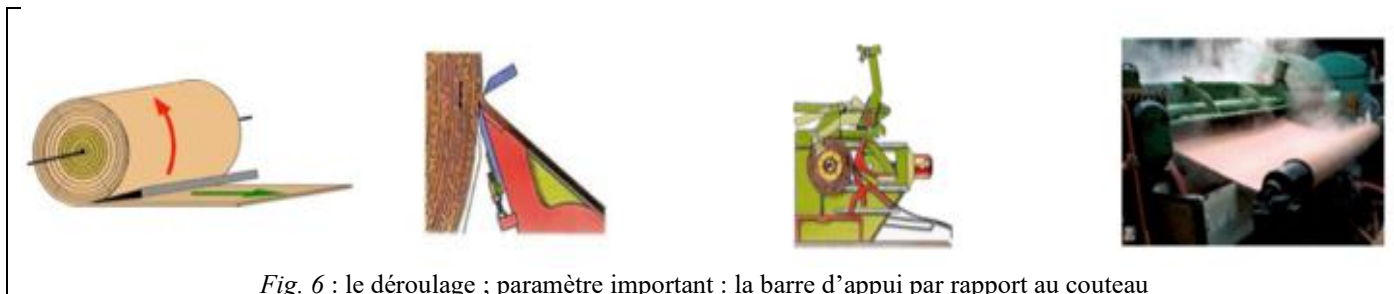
le déroulage ; paramètre important : la barre d'appui par rapport au couteau
